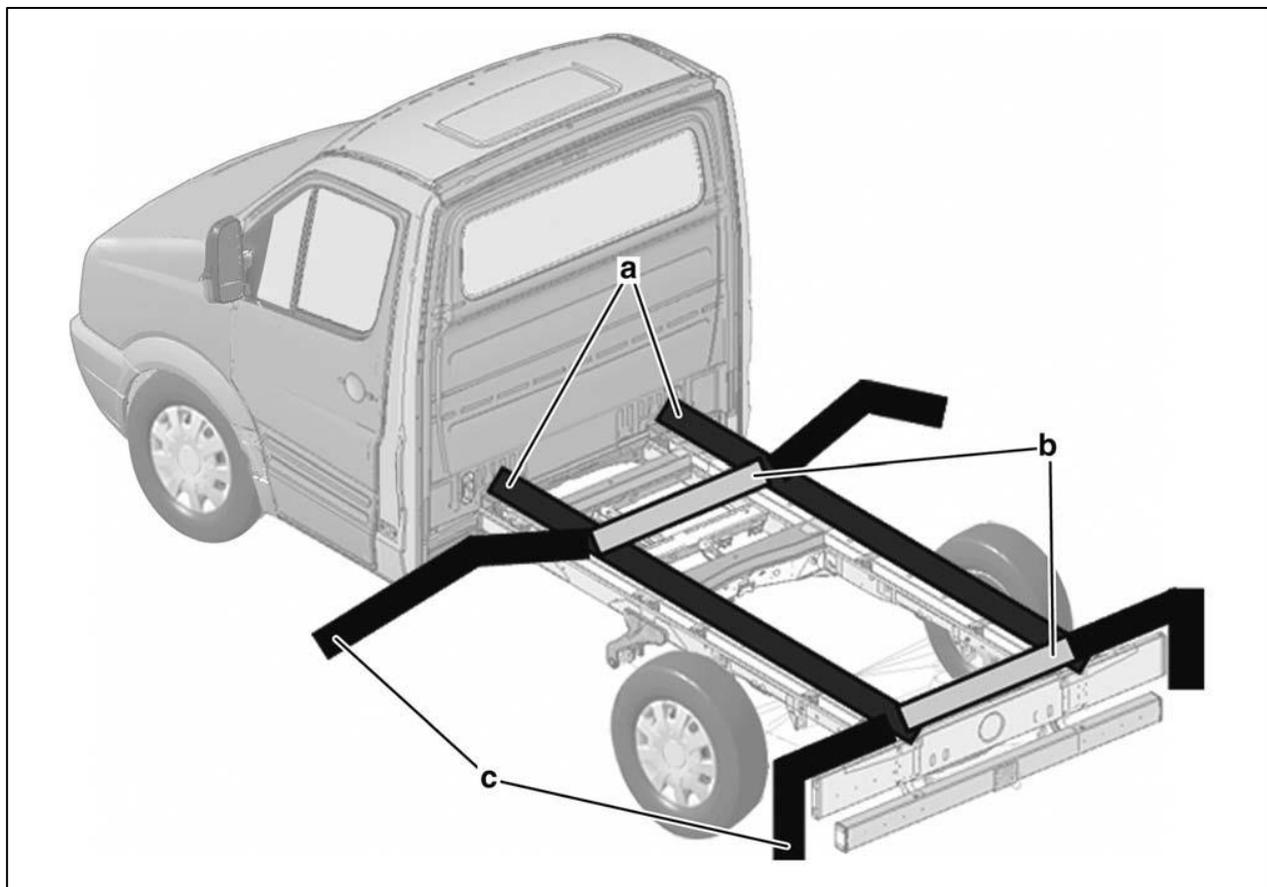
fissaggio del telaio di montaggio alle mensole della sovrastruttura
